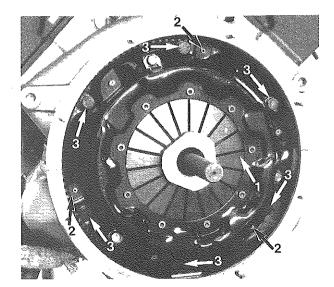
1 - Molle a diaframma Diaphragm springs
